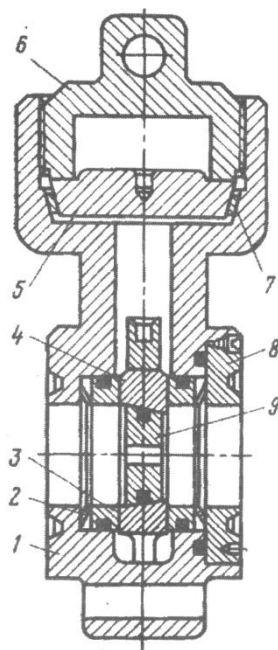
Штуцер быстросъемный для фонтанной арматуры высокого давления (ЩБА-50-70): 1 – корпус, 2 – тарельчатая пружина, 3 – боковое седло, 4 – обойма, 5 – крышка, 6 – нажимная гайка, 7 – прокладка, 8 – гайка боковая, 9 – штуцерная металлокерамическая втулка.
